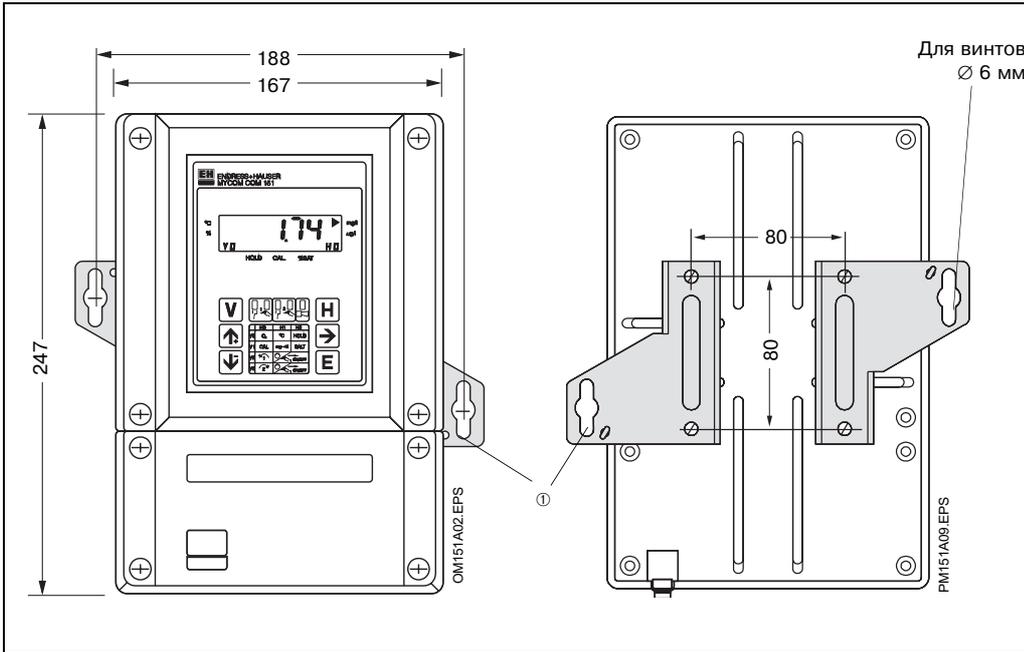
Габаритные размеры (слева) МУСОМ COM 151
